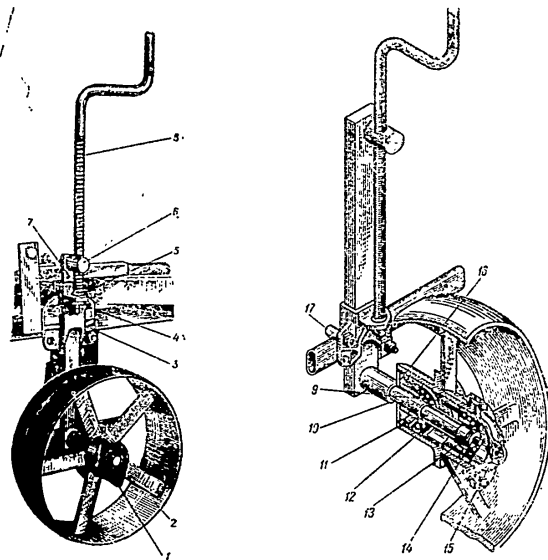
Опорное колесо: 1 — колпак; 2 — колесо; 3 — державка стойки; 4 — шайба; 5 — шайба; 6 — гайка; 7 — стойка колеса; 8 — винт; 9 — ступица; 10 — полуось; 11 — сальник резиновый; 12 — шарикоподшипник; 13 — шайба стопорная; 14 — гайка; 15 — масленка; 16 — отражатель; 17 — скоба
